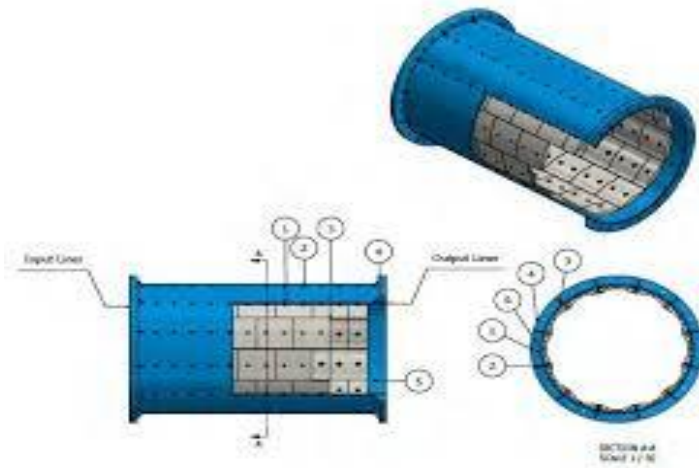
Prinsip Kerja Mesin *Ball Mill
